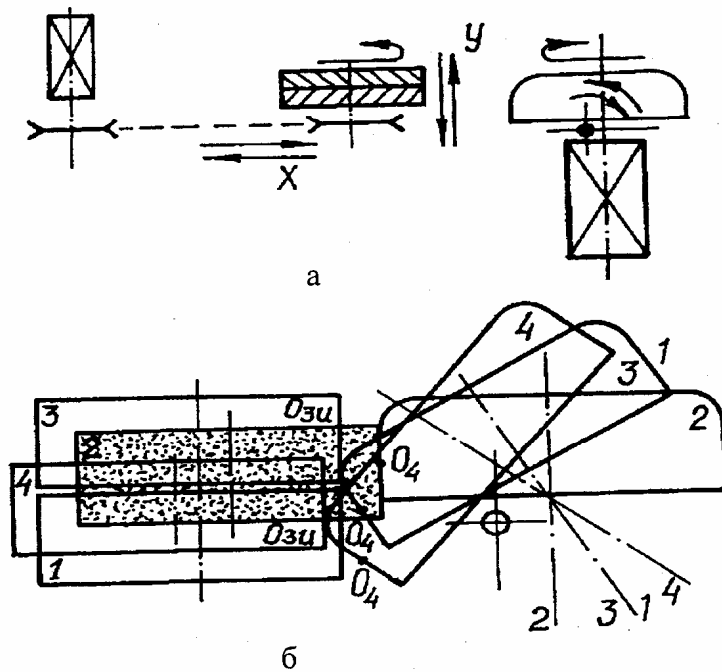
Схема движения инструмента и детали при обработке наружной поверхности (а) и положение инструмента и детали в процессе обработки (один цикл) (б).
